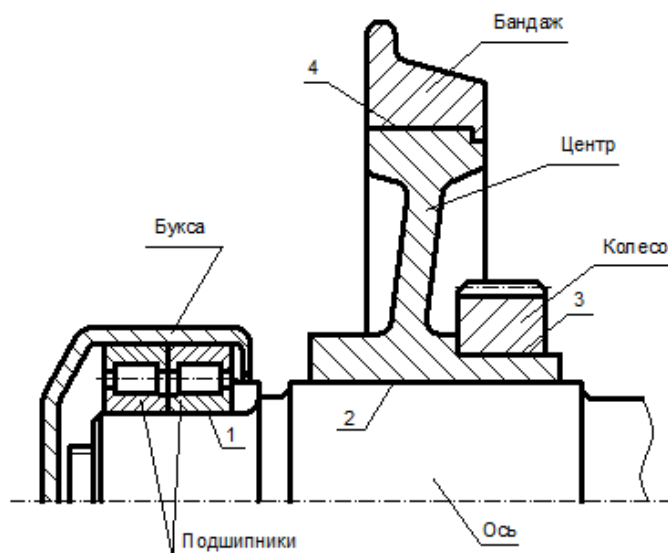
Соединения с натягом локомотивной колёсной пары
